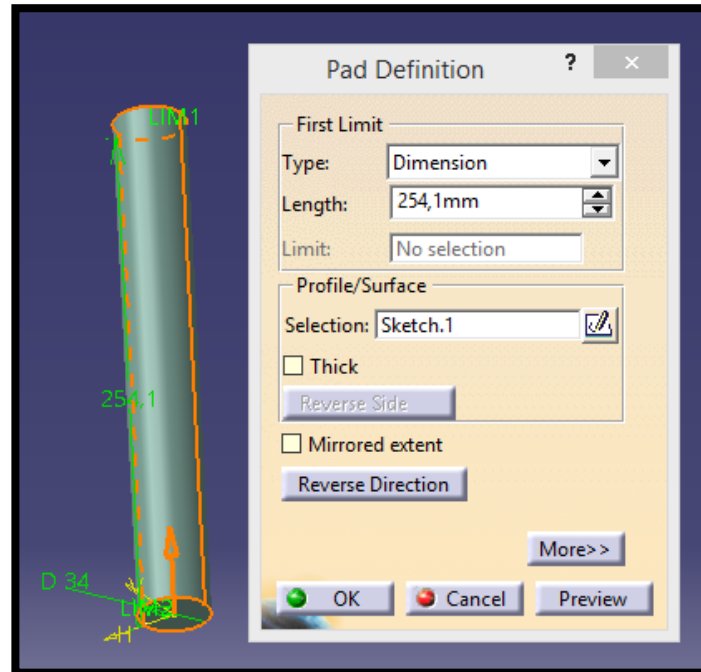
Seat mounting frame 11: Pad pieza 1 amortiguador
